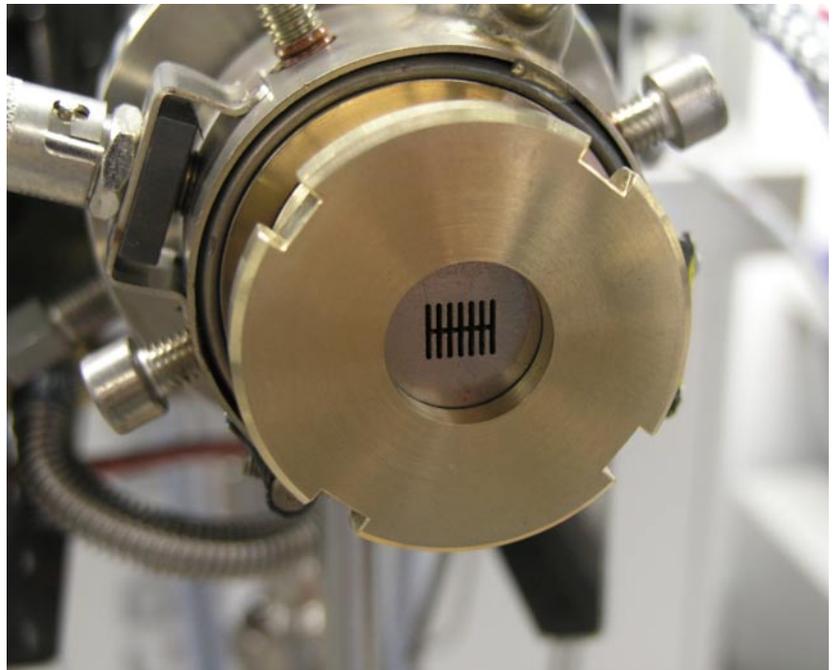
Werkzeug (Düse) für kammähnliches Profil – Stegbreite 0,70 Millimeter.
